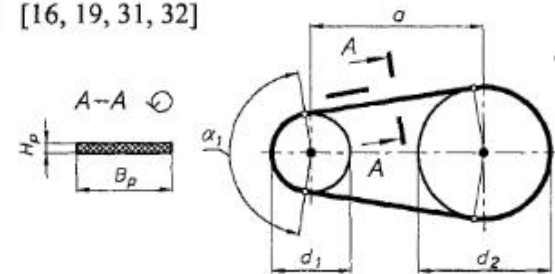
Схема и основные размеры плоскоремненной передачи
